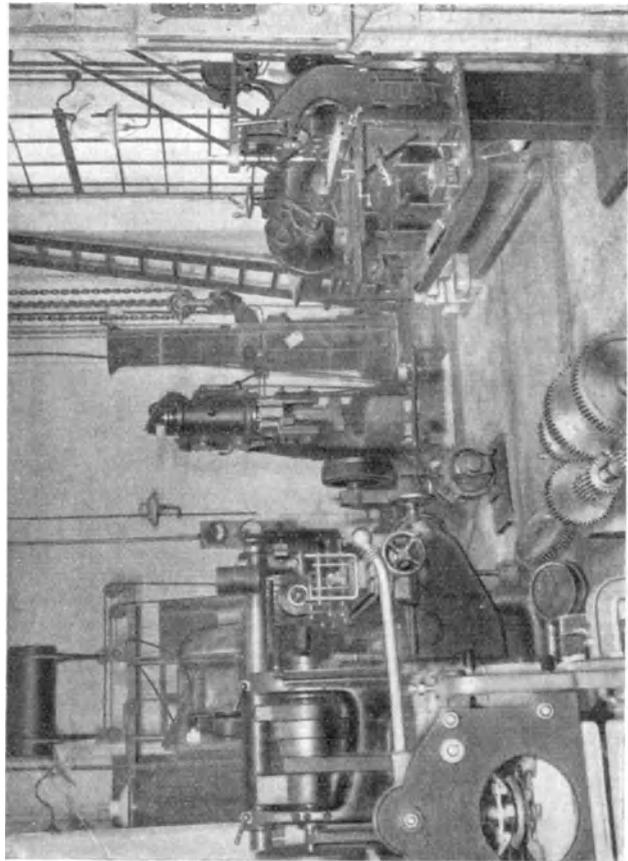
Anbau: Fräsmaschinen und Schmiedehammer.
